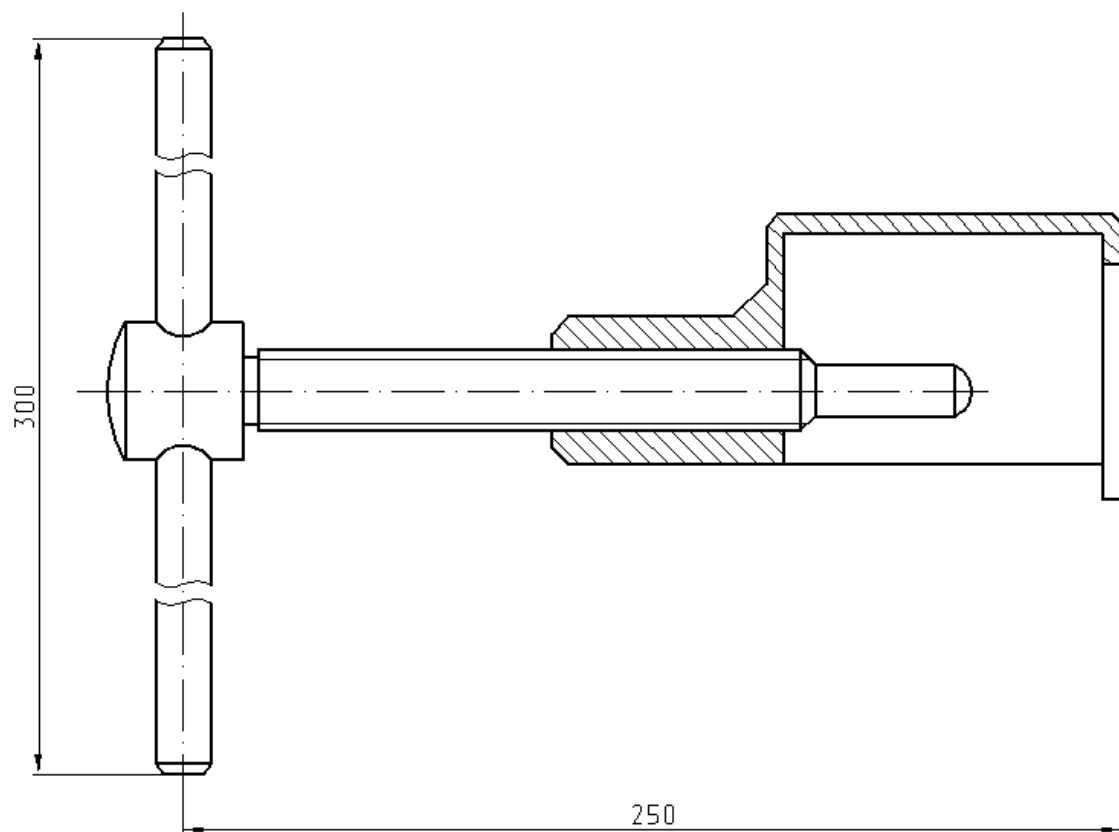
3М 7814-5118-01, Съемник звездочки коленчатого вала
